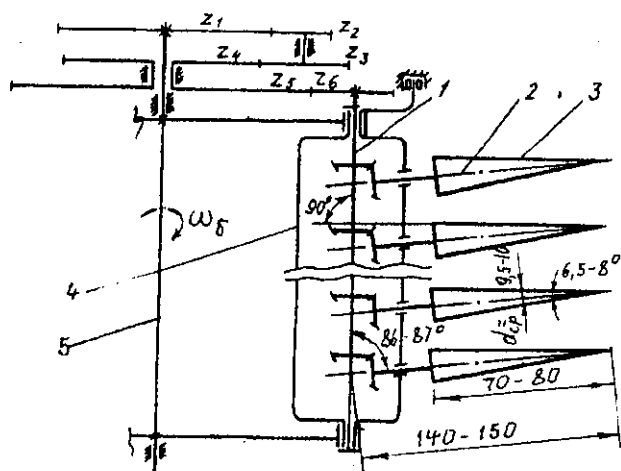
Схема расположения шпинделей в кассете: 1-вал кассеты; 2-ось симметрии шпинделя; 3-верхняя образующая поверхности конического шпинделя; 4-кассета; 5-вал барабана.
